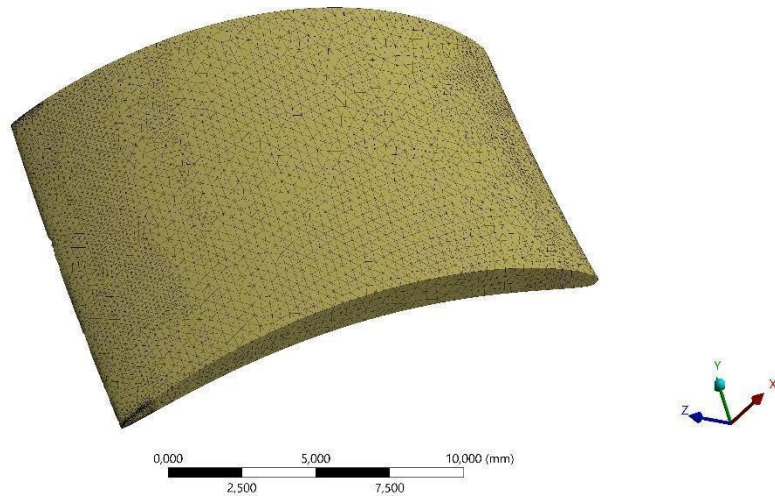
Model Bölümü İçerisinde Türbin Rotor Malzemesinin Seçilmesi
